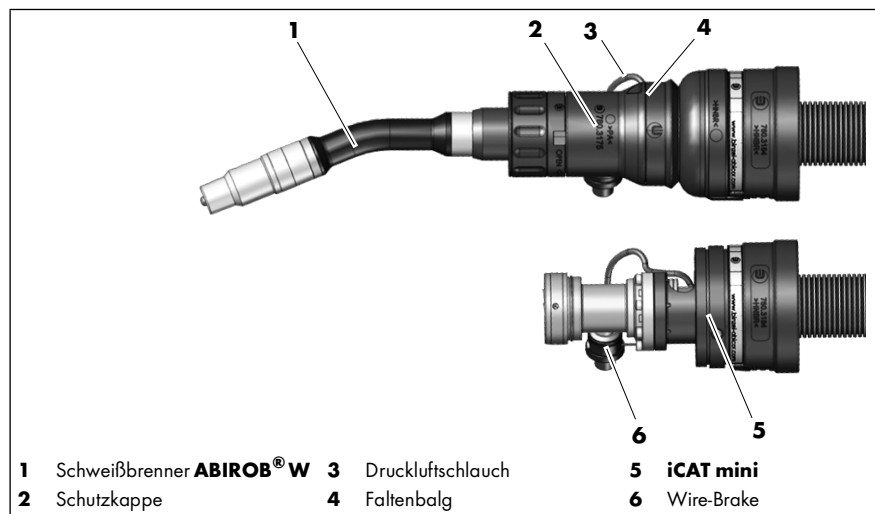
Reinigung – iCAT mini mit Wire-Brake und Schweißbrennerhals ABIROB® W
